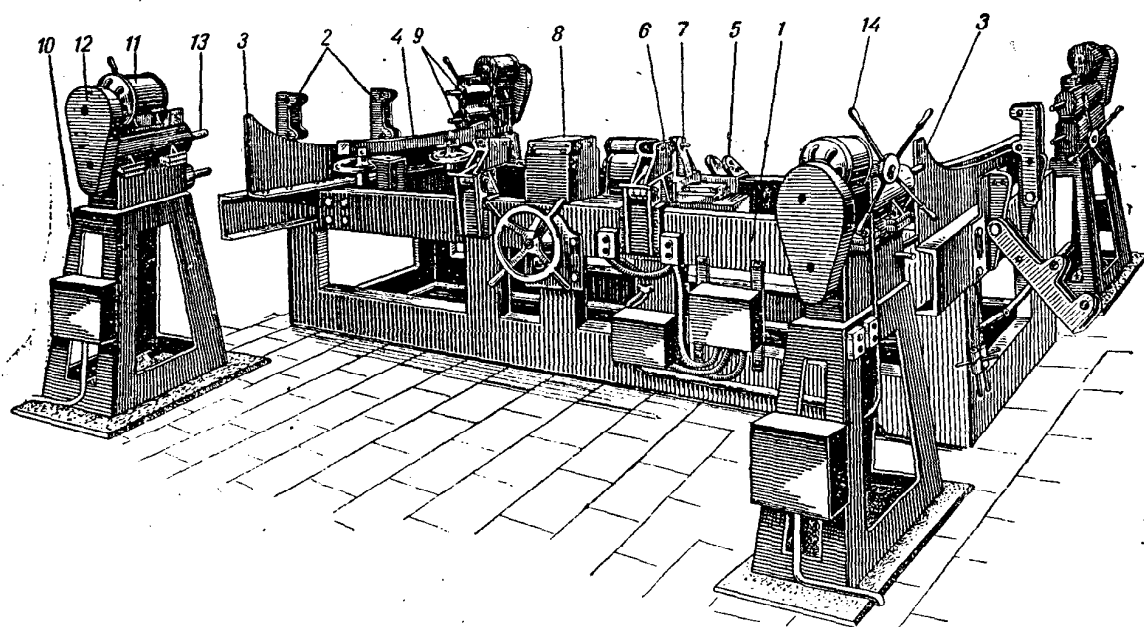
Общий вид агрегатно-разделочного станка центроплана с порталным краном.
